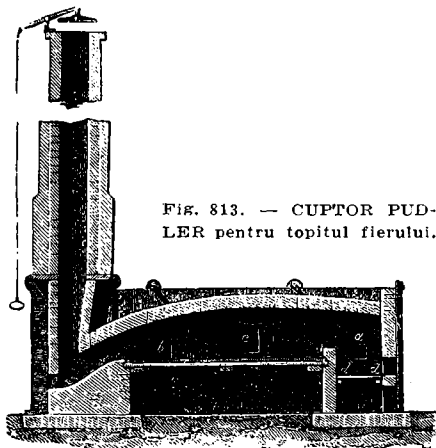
CUPTOR PUDLER pentru topitul fierului.
